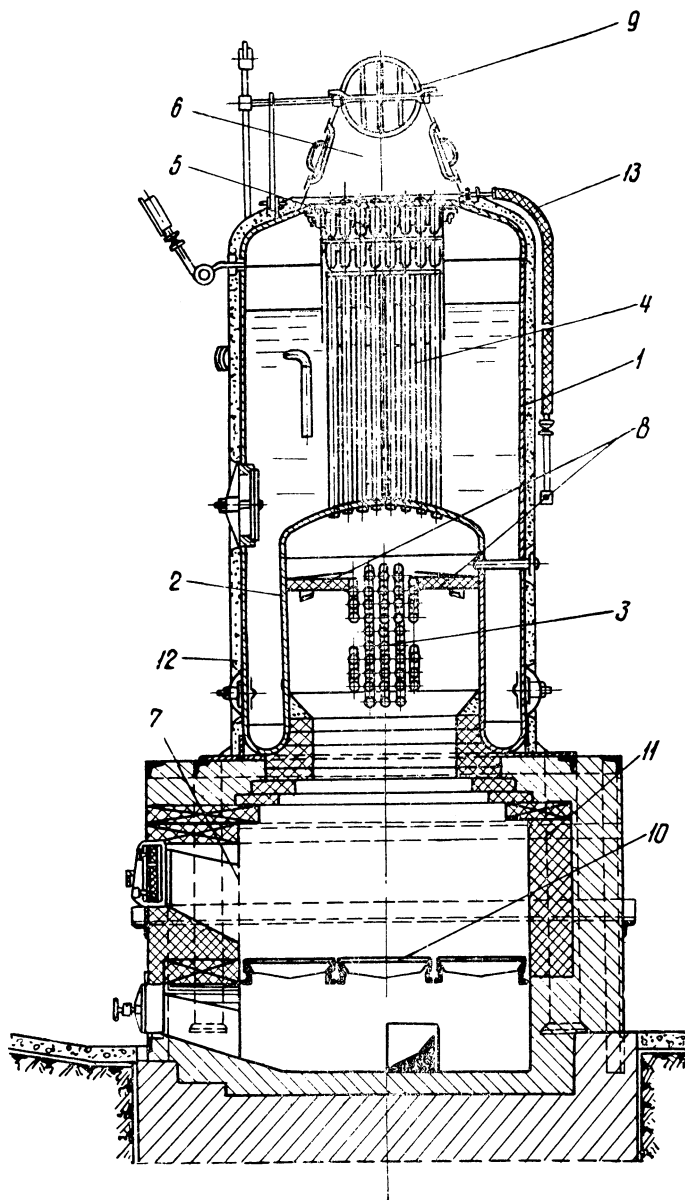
Вертикально-цилиндрический котел ВГД
